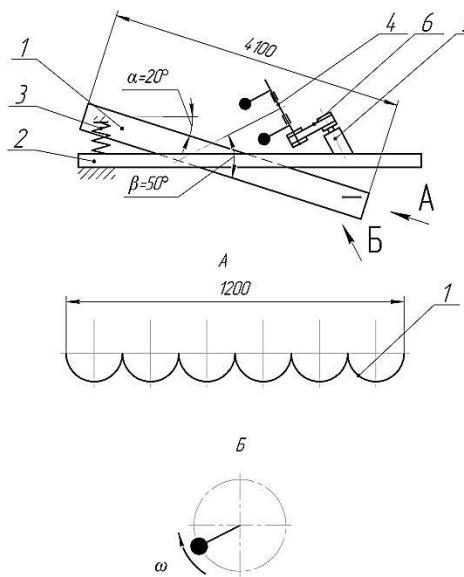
Динамічна схема установки ОЖВ для віброзміцнювальної обробки сиріх окатишів: 1 – орган робочий; 2 – рама опорна; 3 – амортизатори; 4 – вібратор дебалансний; 5 – електродвигун; 6 – передача клинопасова
